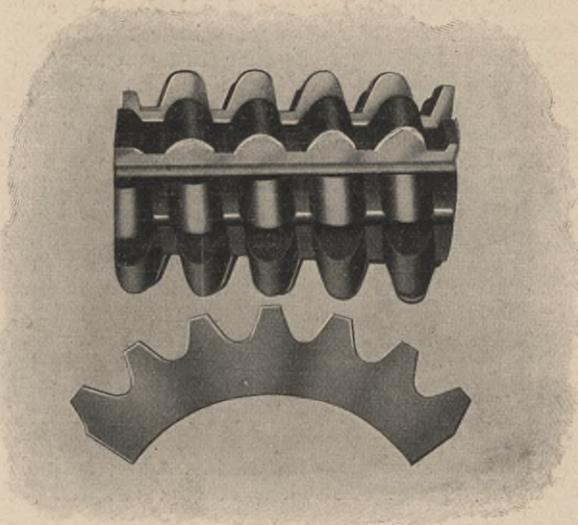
Auf der Abwälz-Fräsmaschine gefrästes Kettenrad
